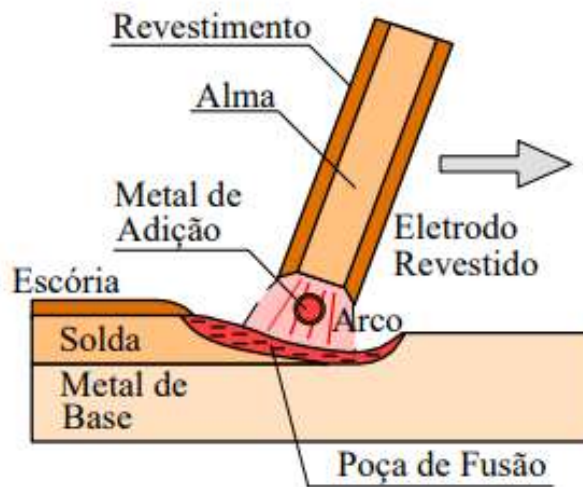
Desenho esquemático do processo de soldagem por eletrodo revestido.
